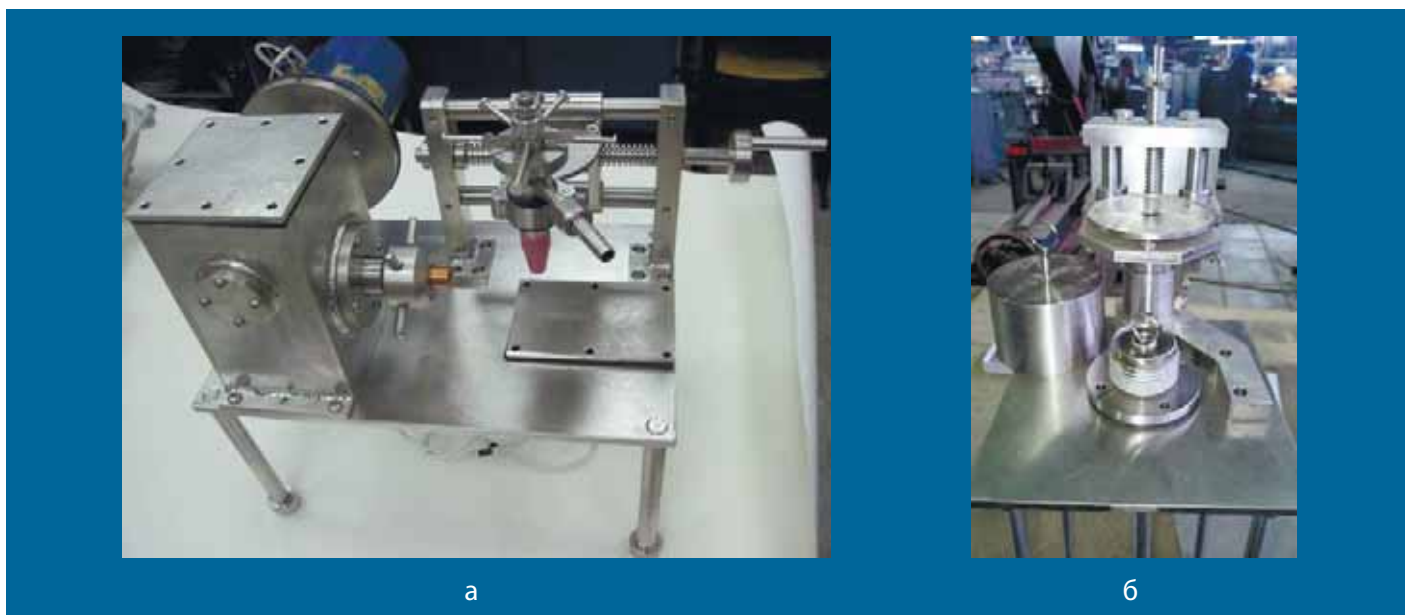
Внешний вид установок сварки (а) и сборки мишени трансплутониевых элементов (б)
